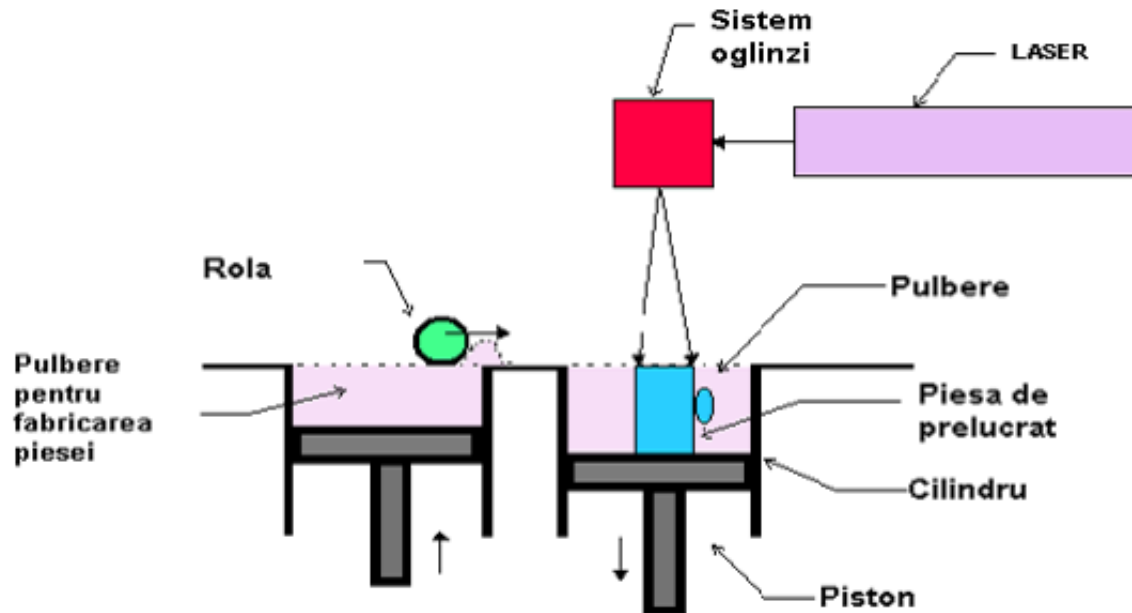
Sinterizarea selectivă cu laser [RAD 12]
